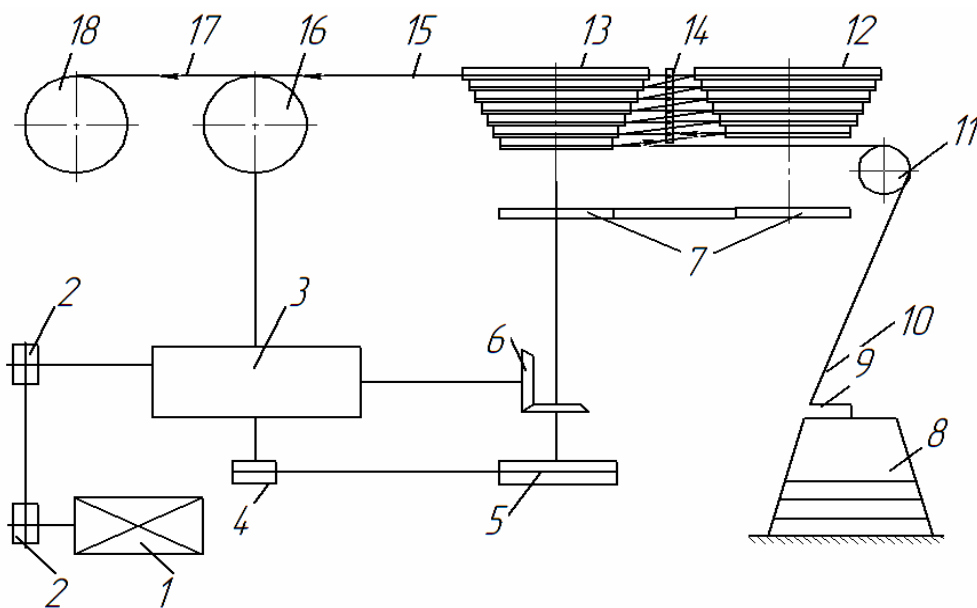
Принципова схема волочильного стану із ковзанням для тонкого дроту: 1 - двигун; 2 - шків; 3 - коробка швидкостей; 4 - шків привода чистового барабана; 5 - шків привода барабанів; 6 - конічна передача; 7 - циліндрична передача; 8 - нерухома розмоточна фігурка; 9 - поводок; 10 - заготовка; 11 - ролик; 12 - напрямний ступінчатий шків; 13 - тягнучий ступінчатий шків; 14 - волокотримач; 15 - готовий дріт; 16 - чистовий барабан; 17 - поводок для укладання витків дроту; 18 - катушка.
